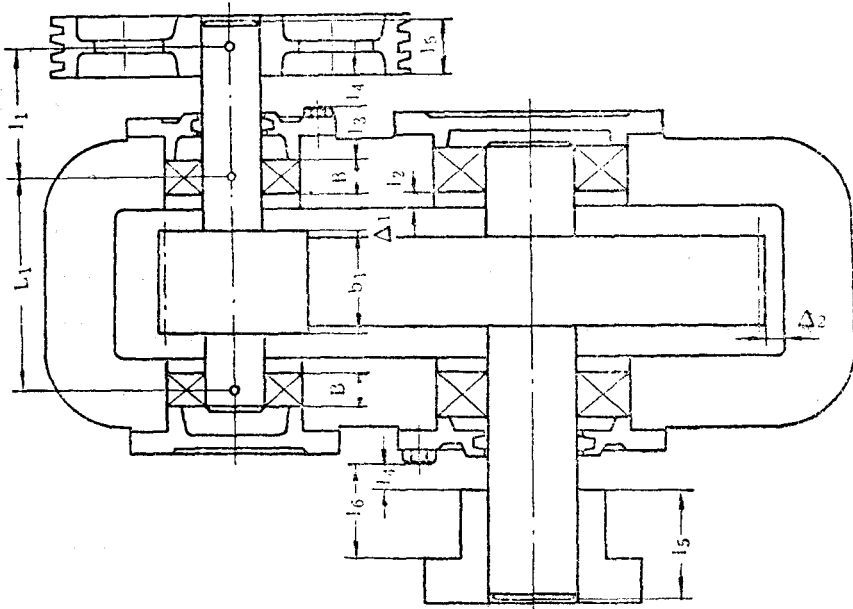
单级圆柱齿轮减速器零件的位置尺寸
